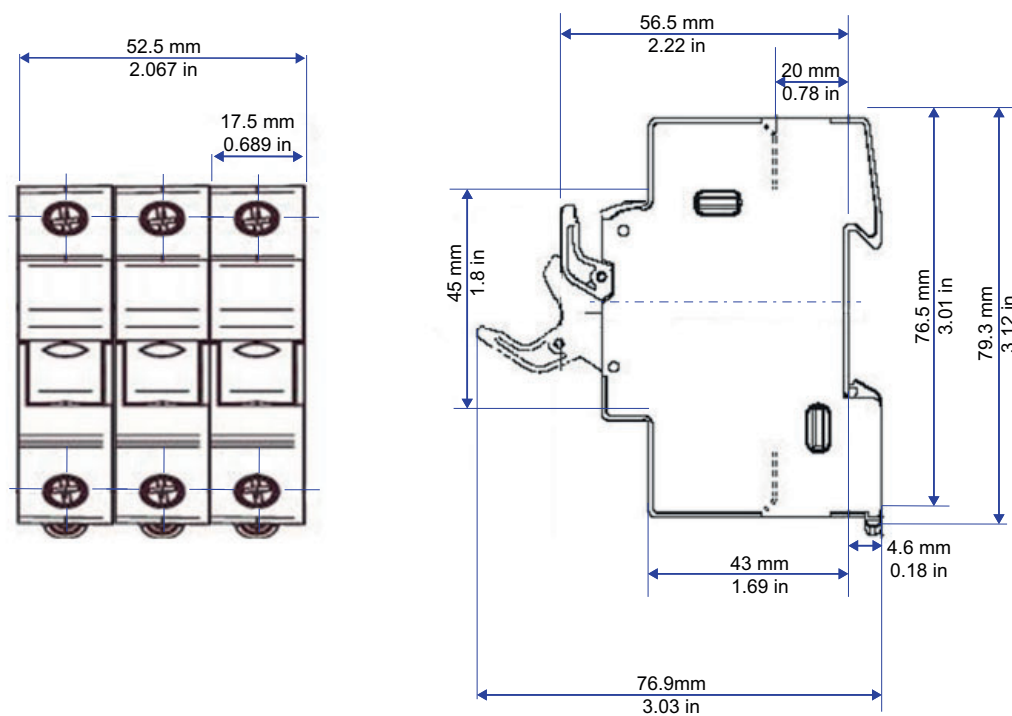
Dimensioni dei portafusibili: CUS103 (10x38 mm)
